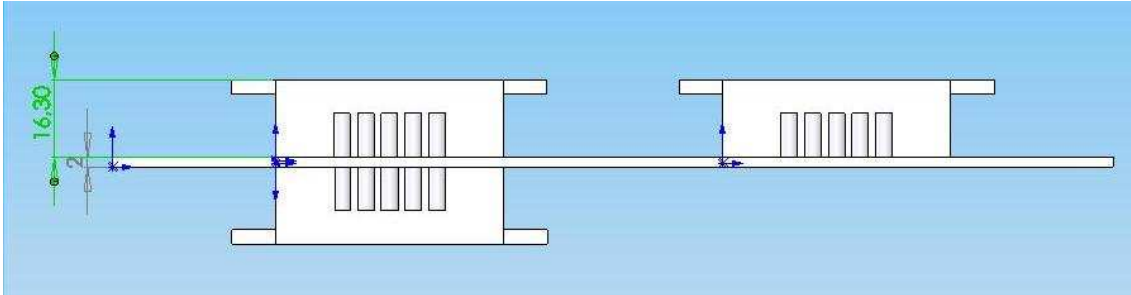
Espesor de la PCB y altura de la carcasa de los drivers.
